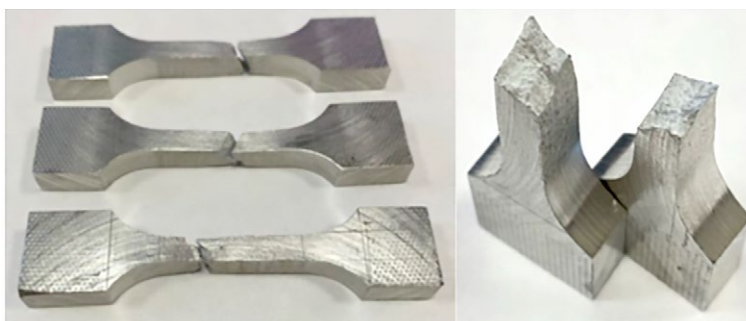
Разорванные образцы из напечатанного алюминия (образец материала без сварки).
